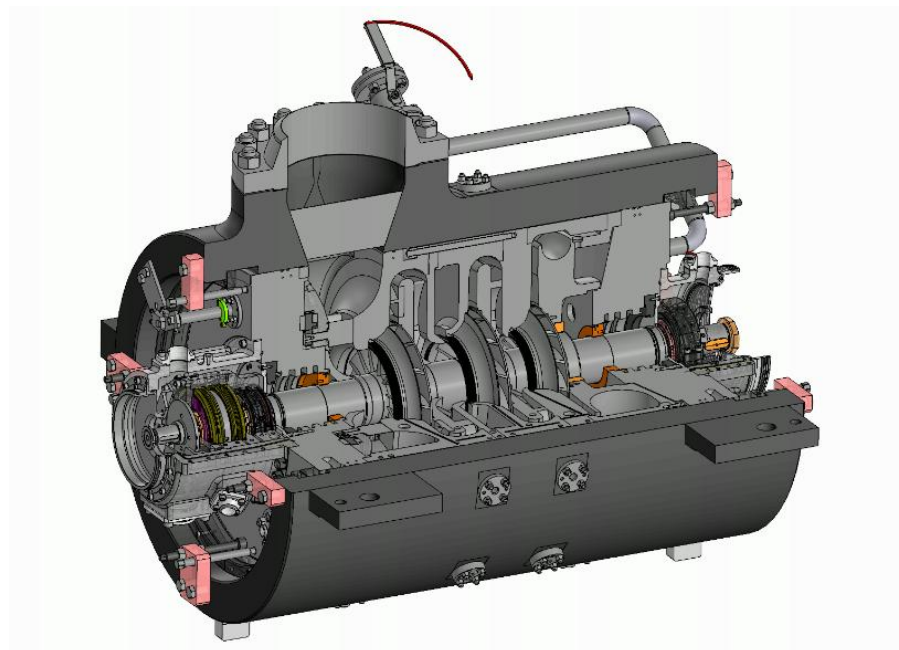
Продольный разрез корпуса сжатия центробежного компрессора 3ГЦ2-135/1,5-4,6 УХЛ4.
